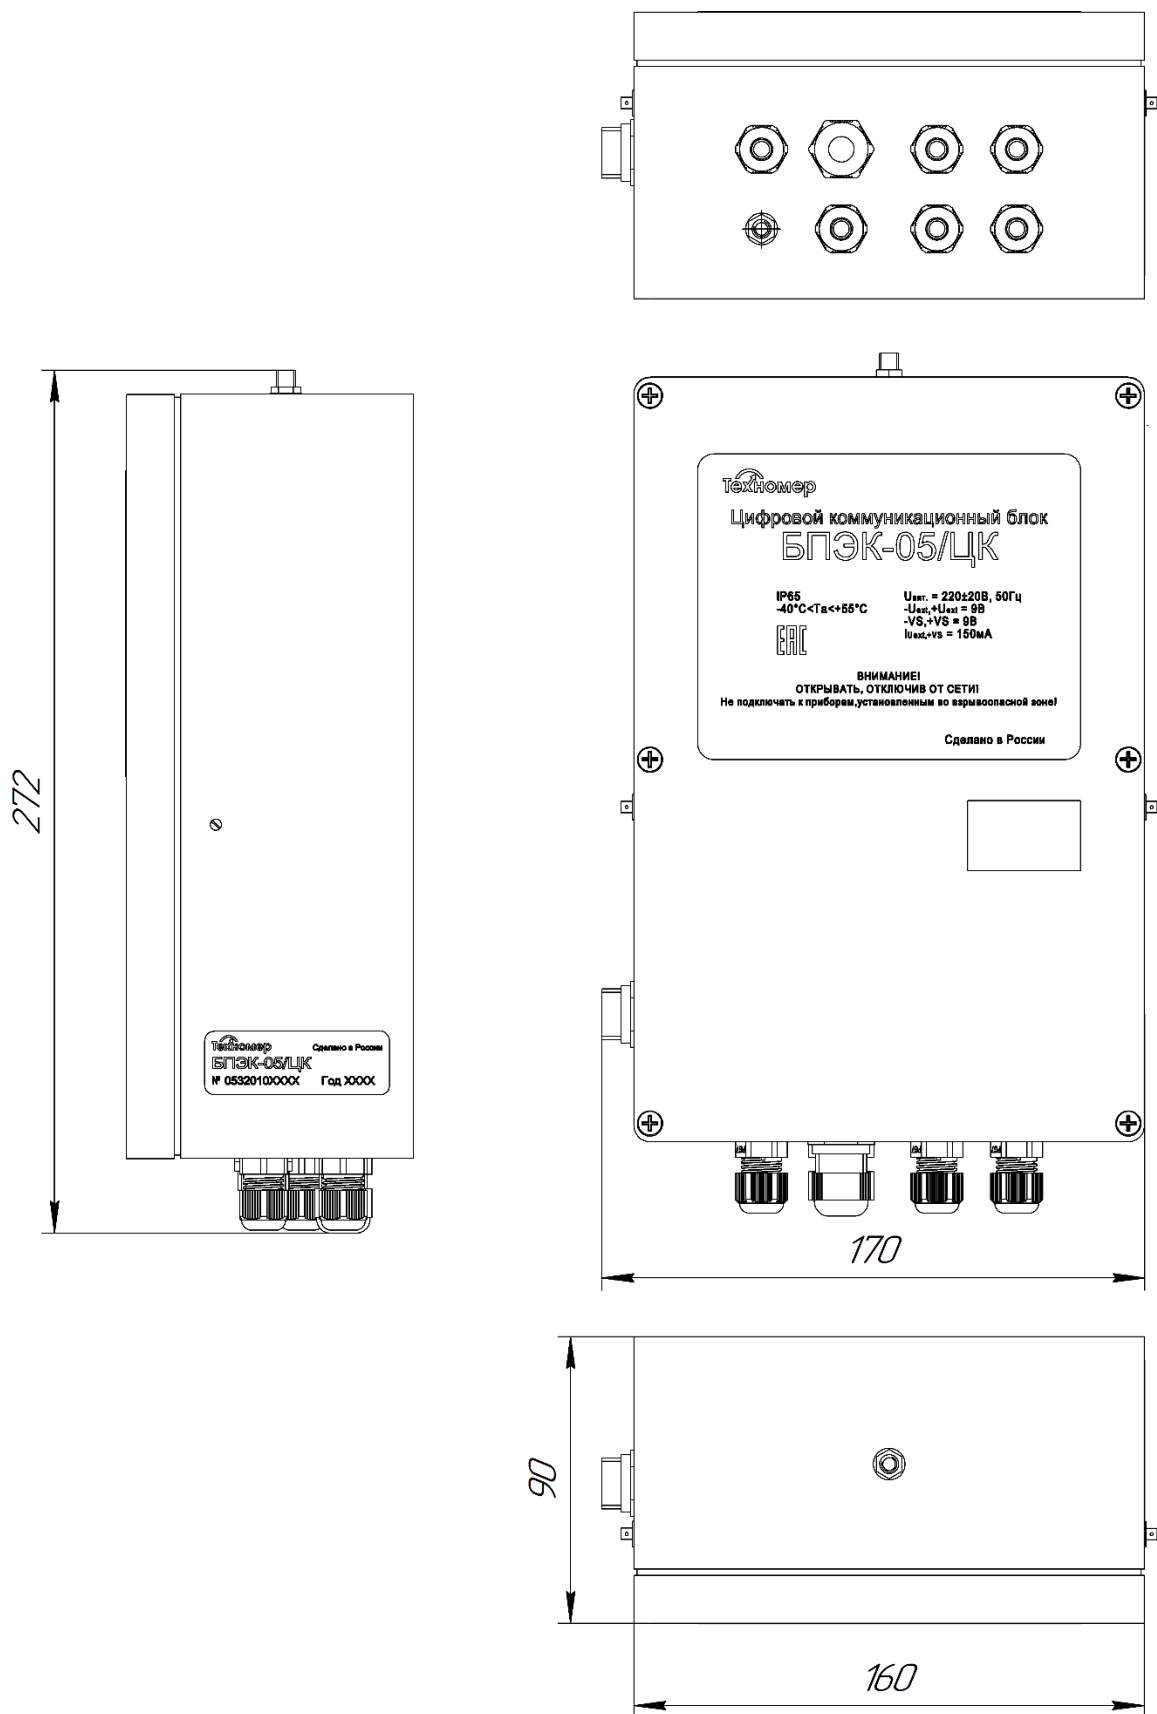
Габаритные размеры блока БПЭК-05/ЦК
